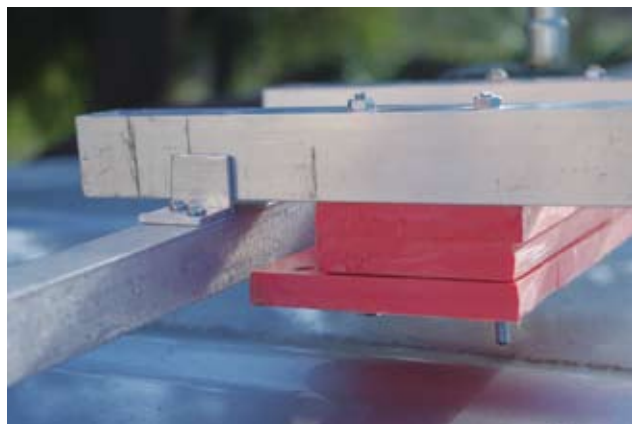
Incastro del "binario" sulla traversa anteriore.
